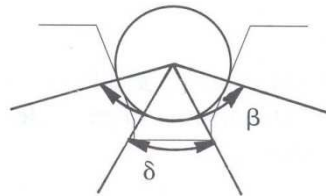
Garganta Trapezoidal, ángulos de apoyo del cable indicados
